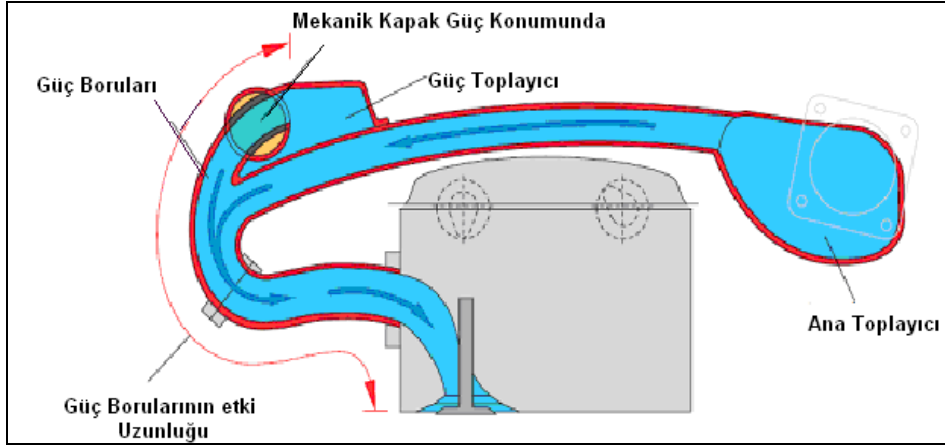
Mekanik emme manifoldunda tork durumu
